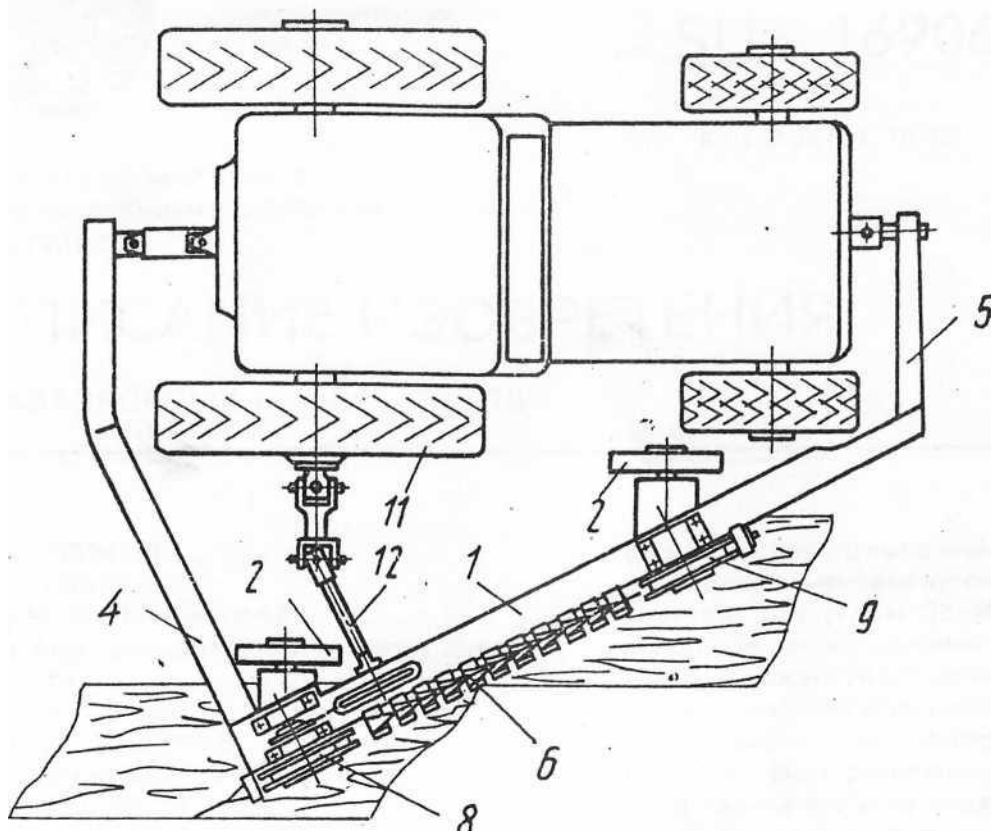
Пристрій для ворухіння валків, вид зверху [10]
